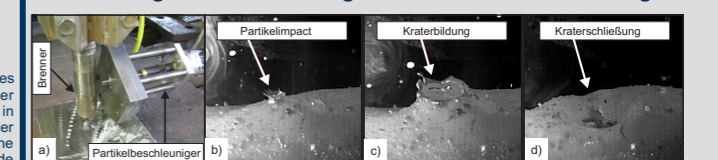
a) Foto des Partikelbeschleunigers adaptiert an einen MSG-Brenner für Auftragschweißungen; b) - d) Aufnahme des Impacts eines Oxidpartikels in eine Metallschmelze mit einer Hochgeschwindigkeitskamera
